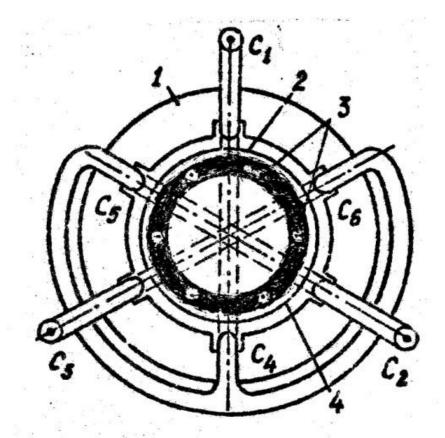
Траверса: I - бугель; 2 - выступ; 3 стягивающий винт; 4 - разрез; 5 палец щеткодержателя; 6 - стопорный винт
